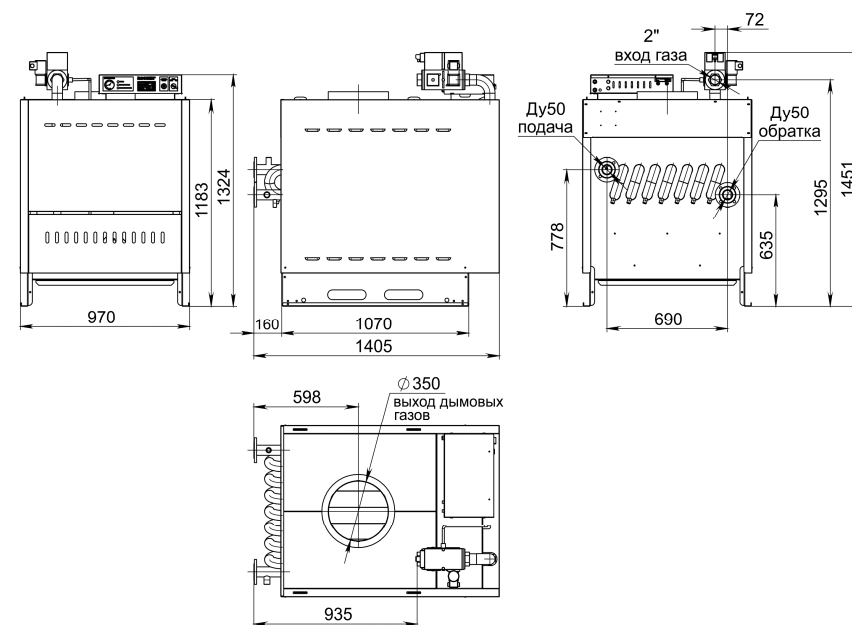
Габаритно-присоединительные размеры котла RSA250
